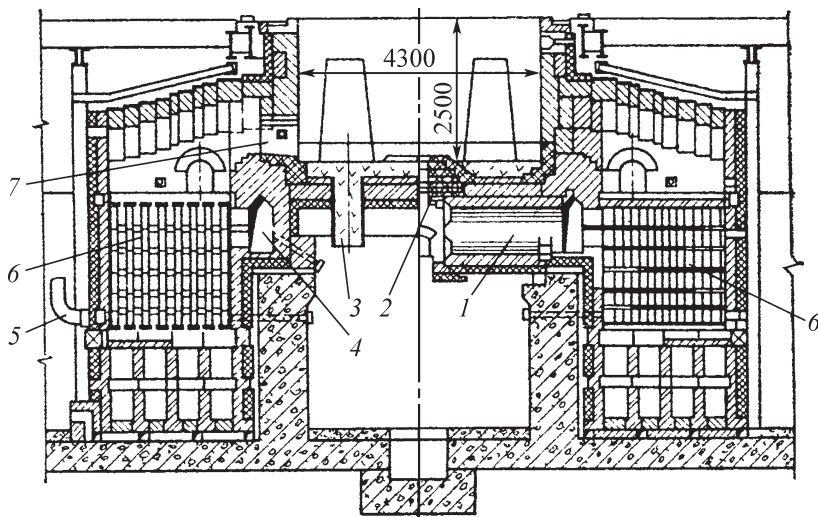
Рекуперативный нагревательный колодец с отоплением из центра подины (крышка снята):
